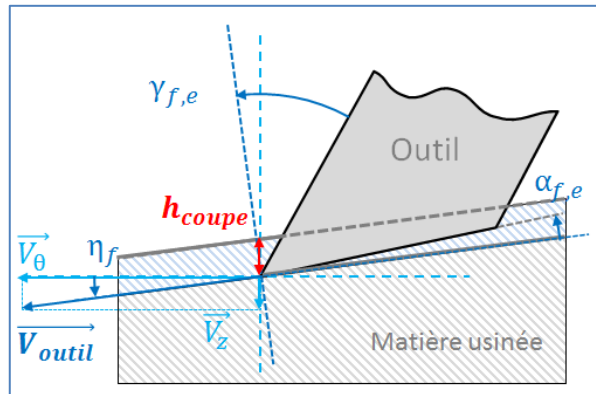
Définition de la hauteur de coupe en perçage conventionnel dans la projection cylindrique de rayon (r) tangente au plan (P_f) .
